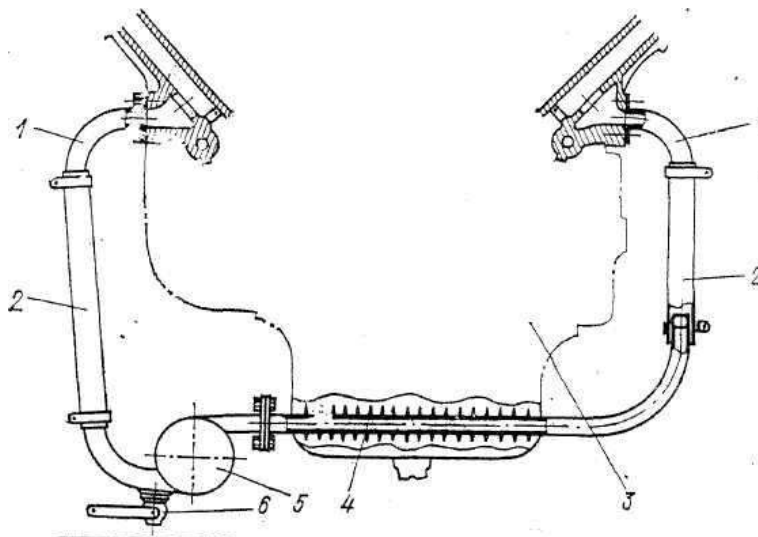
Электронагреватель с теплообменником: 1 – патрубки блока цилиндров; 2 – соединительные шланги; 3 – картер двигателя; 4 – теплообменник; 5 – нагревательный котел; 6 – сливной кран.
